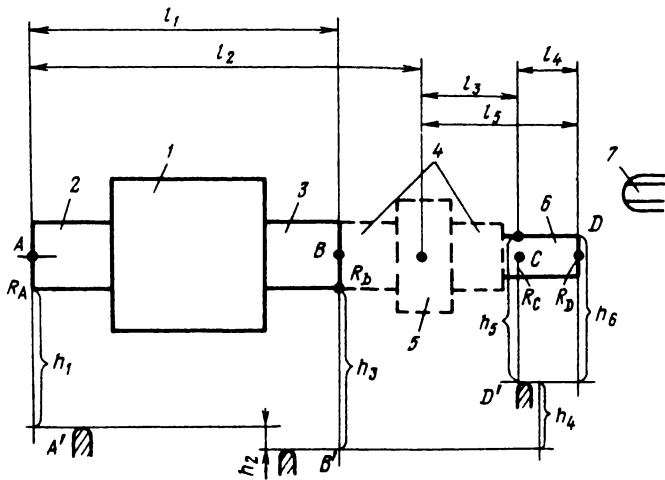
Схема контроля мельниц по высоте без остановки агрегата:
